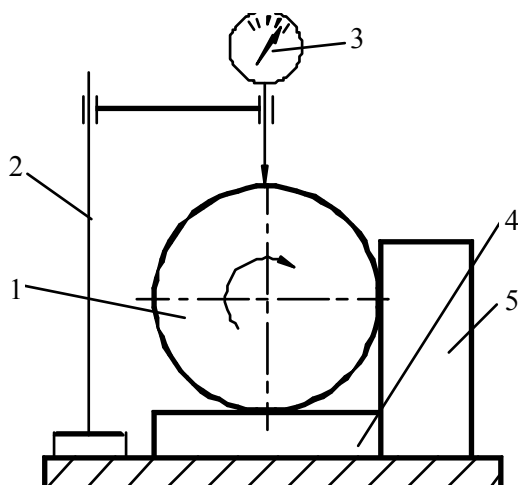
Схема двухточечного измерения отклонения от круглости с непрерывным вращением детали: 1 – измеряемая деталь; 2 – штатив; 3 – измерительная головка; 4 – неподвижная опора; 5 – боковой упор
